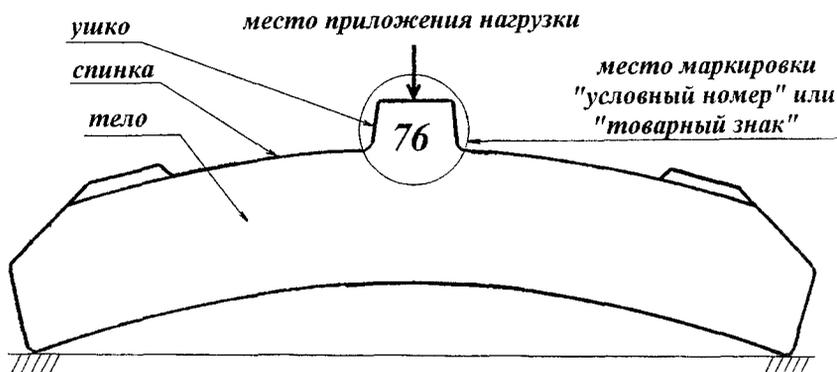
Схема испытания на излом тормозной колодки и место расположения маркировки «условный номер» или «товарный знак» предприятия-изготовителя
